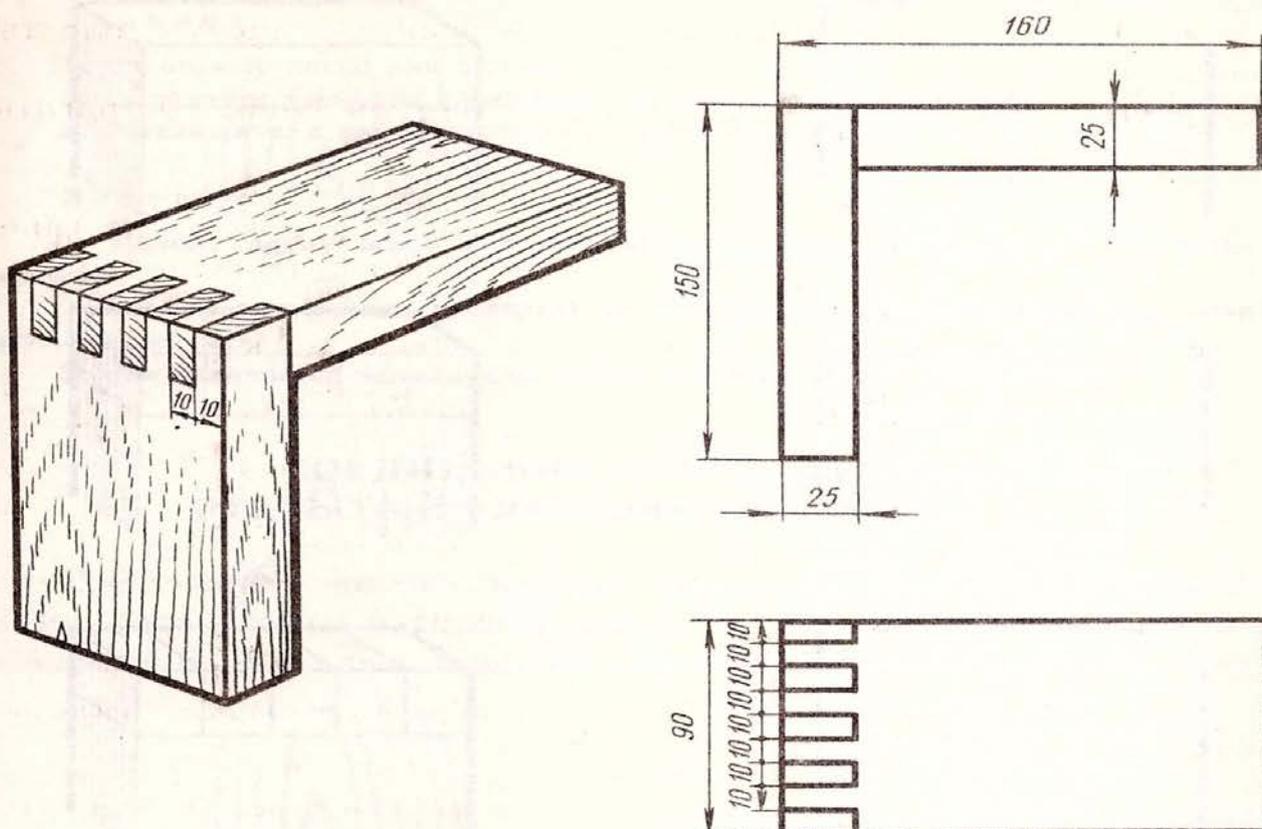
Чертеж ящичного соединения на шип прямой открытый УЯ-1.
